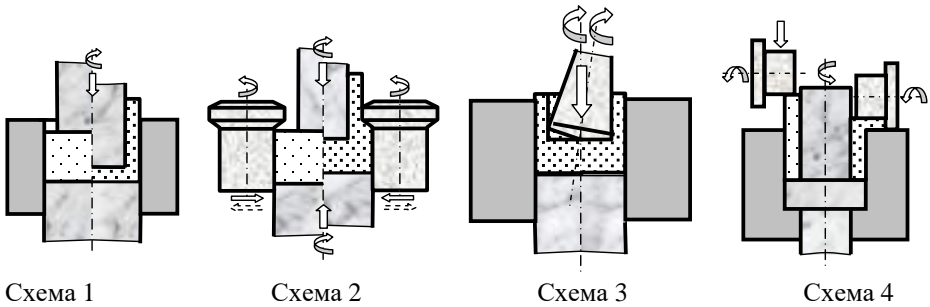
Способи виготовлення порожнистих деталей з різною кінематикою руху інструменту
